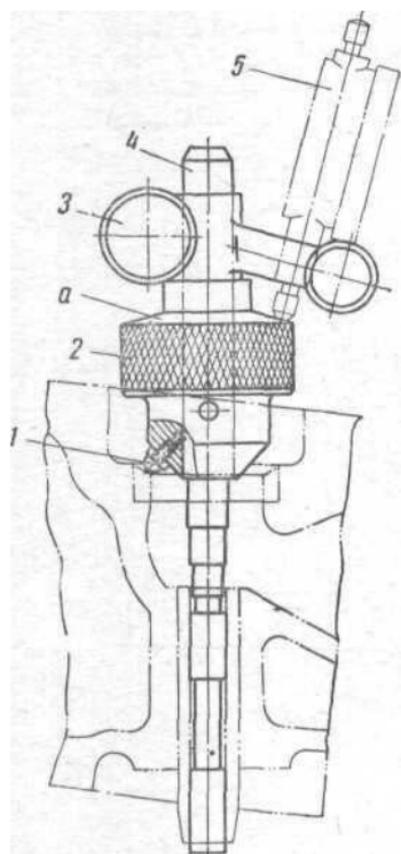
Приспособление для проверки концентричности фаски седла клапана относительно направляющей втулки
